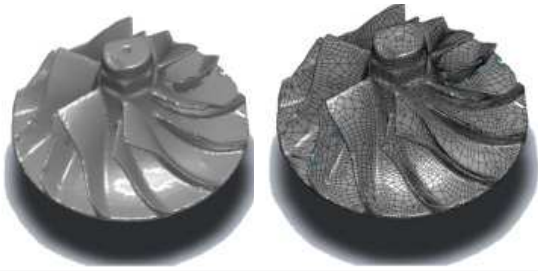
Тривимірна 3D-сітка модель робочого колеса [86]
